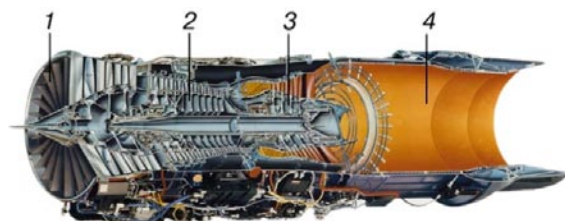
Турбовентиляторный двигатель с форсажной камерой
